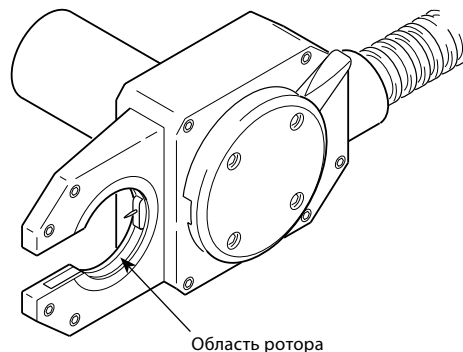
Осмотр открытых поверхностей сварочной головки
